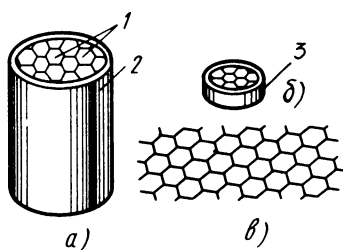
Изготовление сотовых сеток: а — вставка пучка проволок в обойму для протягивания через фильеру, б — резка на диски и шлифовка, в — вытравливание алюминия; 1 — пучок проволок, 2 — обойма, 3 — диск
